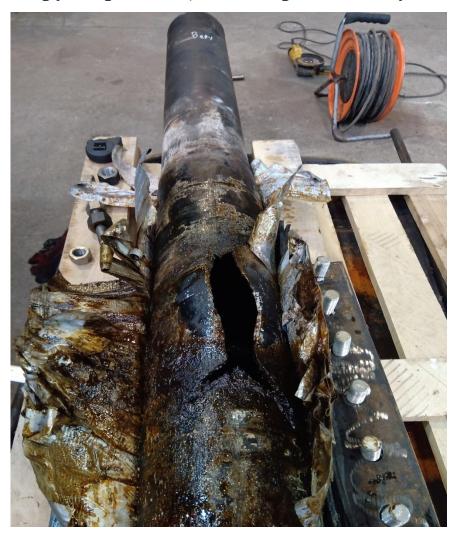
Трубопровод после пожара (на месте разрыва установлен хомут)
